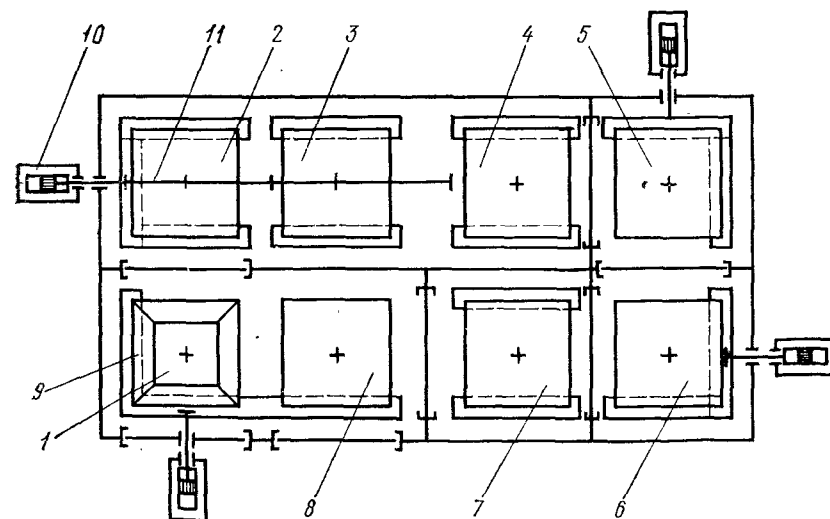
Автоматическая установка для промывки оптических деталей
